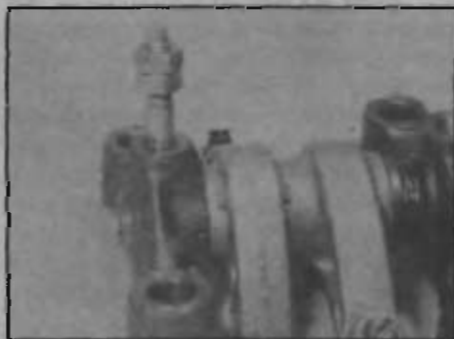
Использование двух гаек для выворачивания шпильки крепления крышки головки цилиндров
